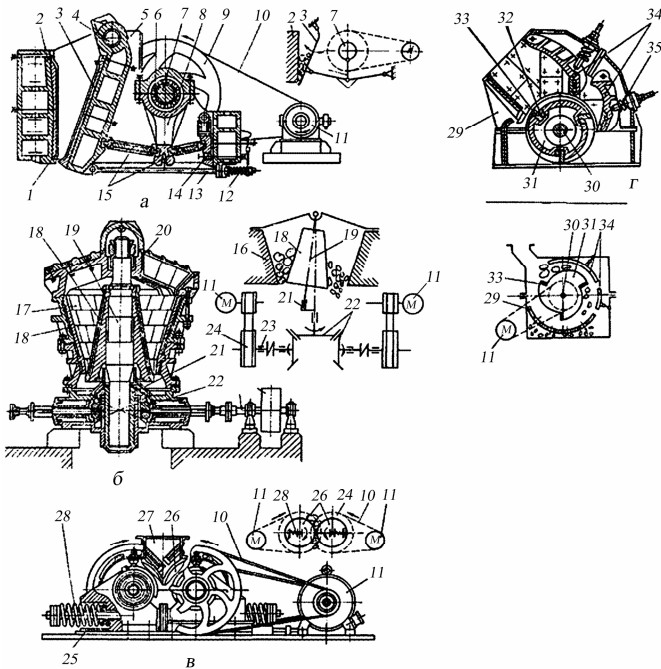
Конструкції й принципові схеми дробарок:
